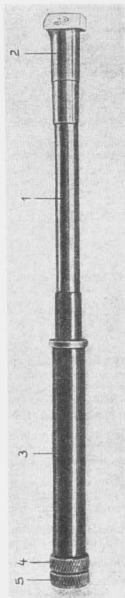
Lauf. 1 = Lauf, 2 = Laufführung, 3 = Laufführung, 4 = Mutter, 5 = Gegenmutter
